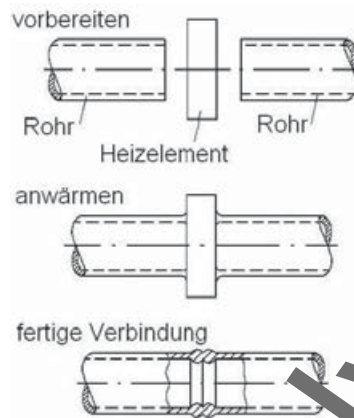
Prinzip des Heizelementstumpfschweißens am Beispiel Rohr.
